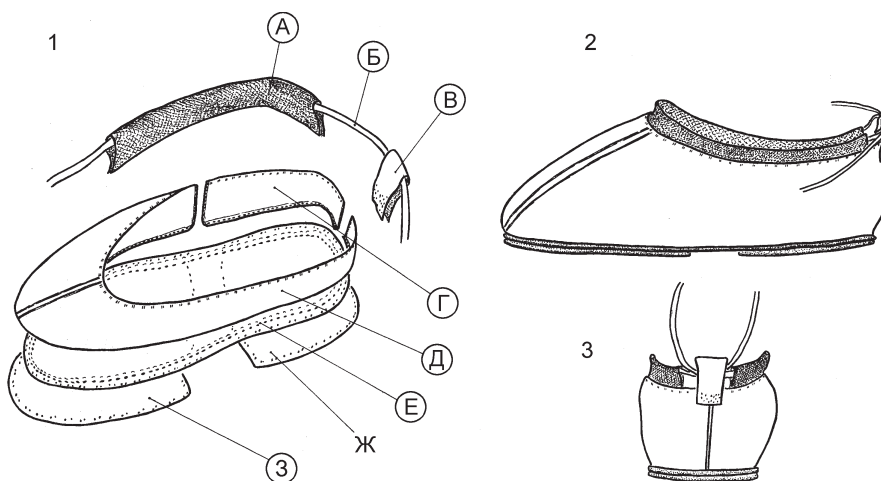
Схема сборки уледей первого варианта. 1 — компоновка деталей: А — тканая обшивка верхнего края; Б — плетеный или вязаный ремешок-обора; В — петля пяточная; Г — пришивное крыло; Д — основа верха; Е — подошва; Ж — пяточная подметка; З — носочная подметка. 2 и 3 — реконструкция, виды сбоку и сзади
